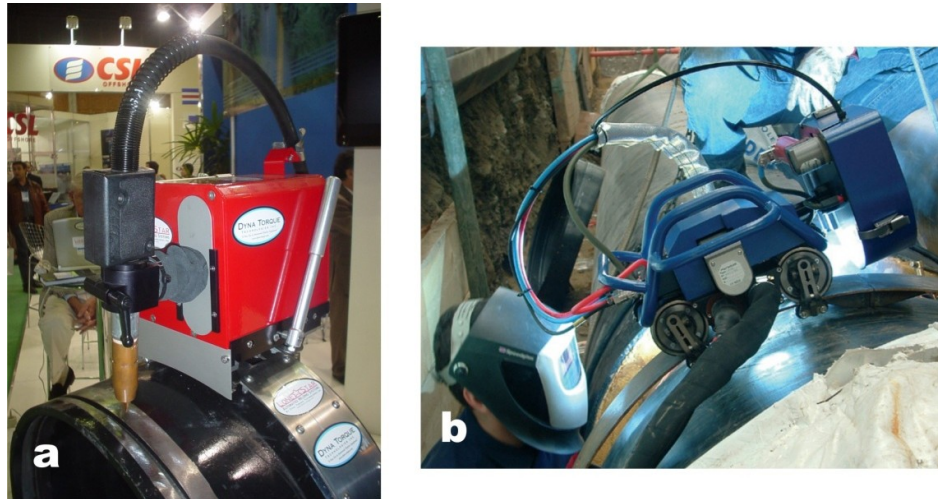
Sistemas para a soldagem orbital. Em (a) manipulador da DYNATORQUE e em (b) da POLYSOUDE
